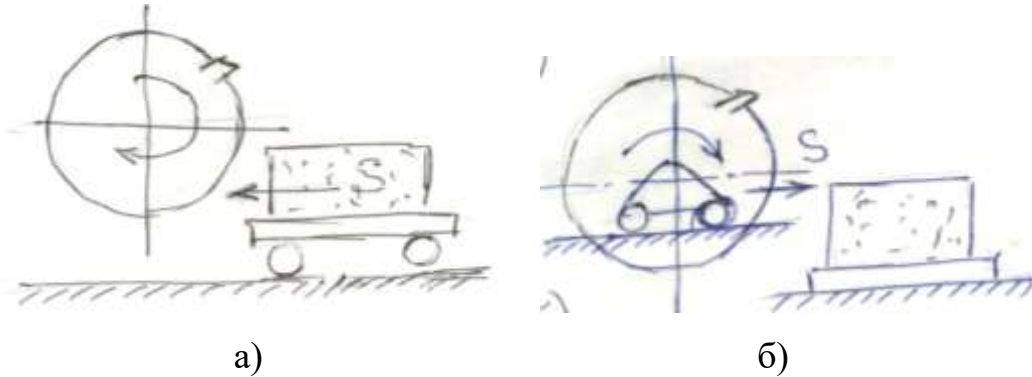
Схеми компоновок розпилювальних верстатів:
